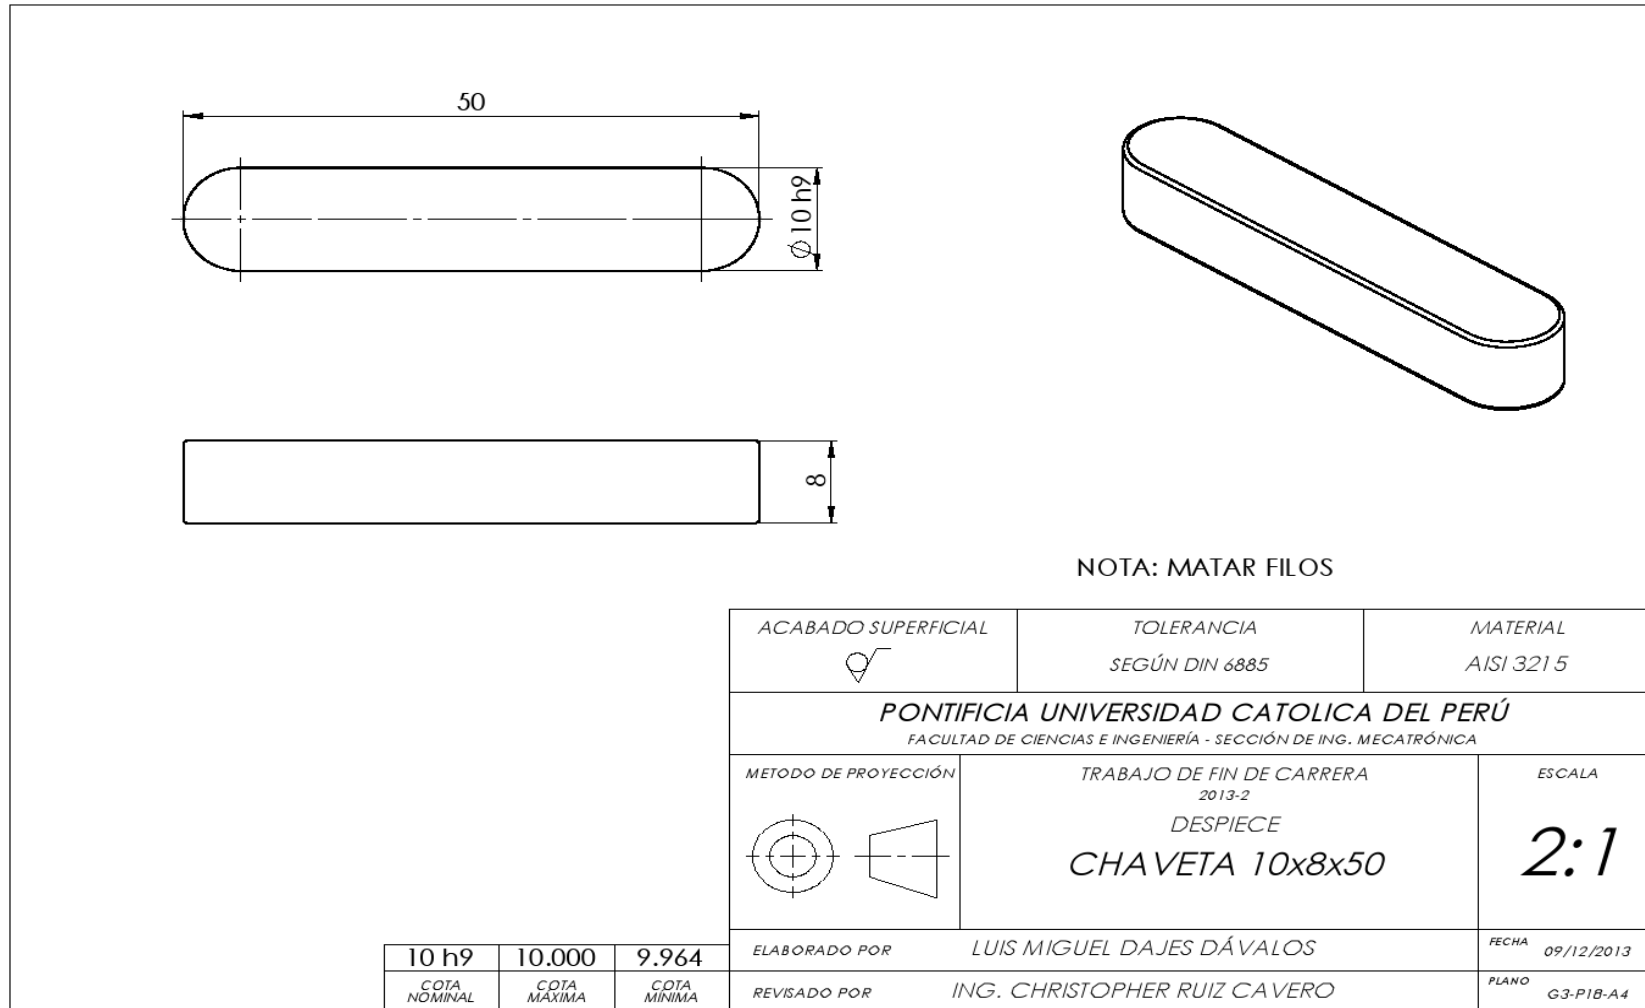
Plano de despiece de la chaveta del engranaje 1. Fuente: Elaboración propia.
